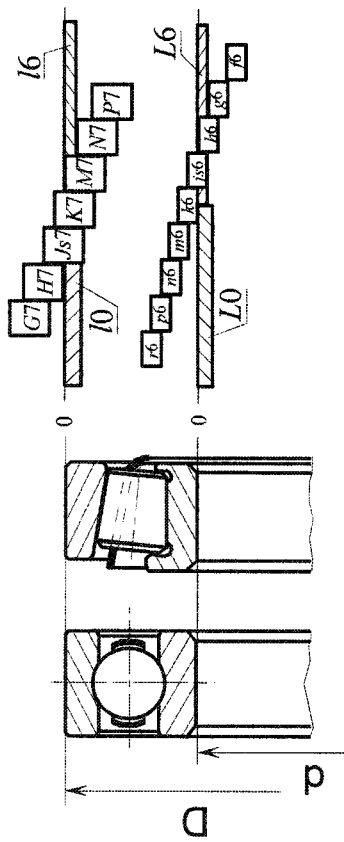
Схема расположения рекомендуемых полей допусков посадочных размеров для подшипников классов точности 0 и 6
